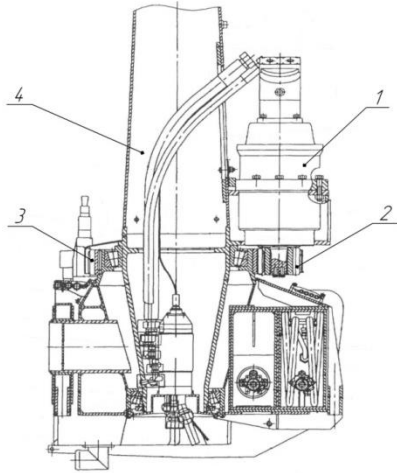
Опорно-поворотний пристрій на основі гідромотора та циліндричної передачі
